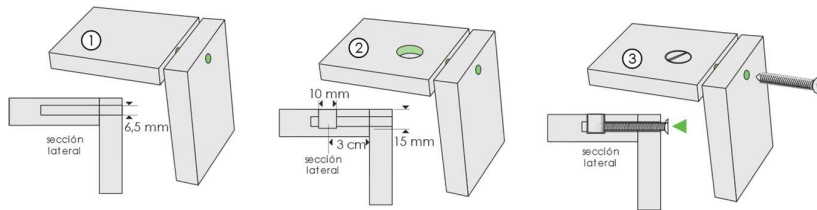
ensamblaje perno roscado fuente: propia elaboración: William Márquez
